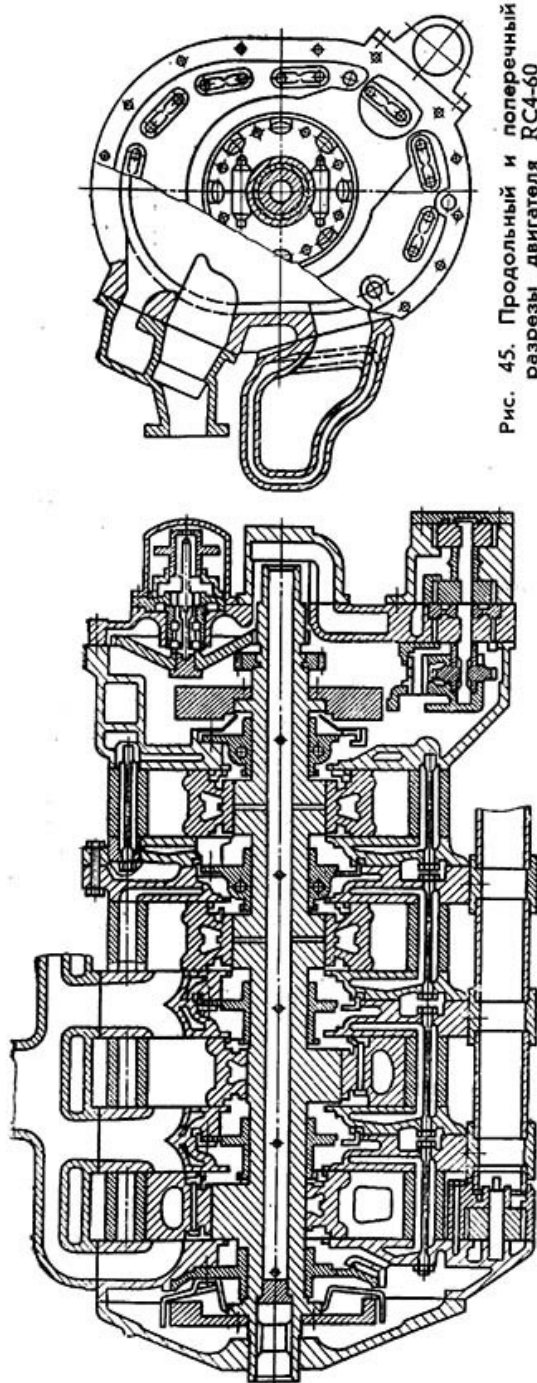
Продольный и поперечный разрезы двигателя RC4-60
